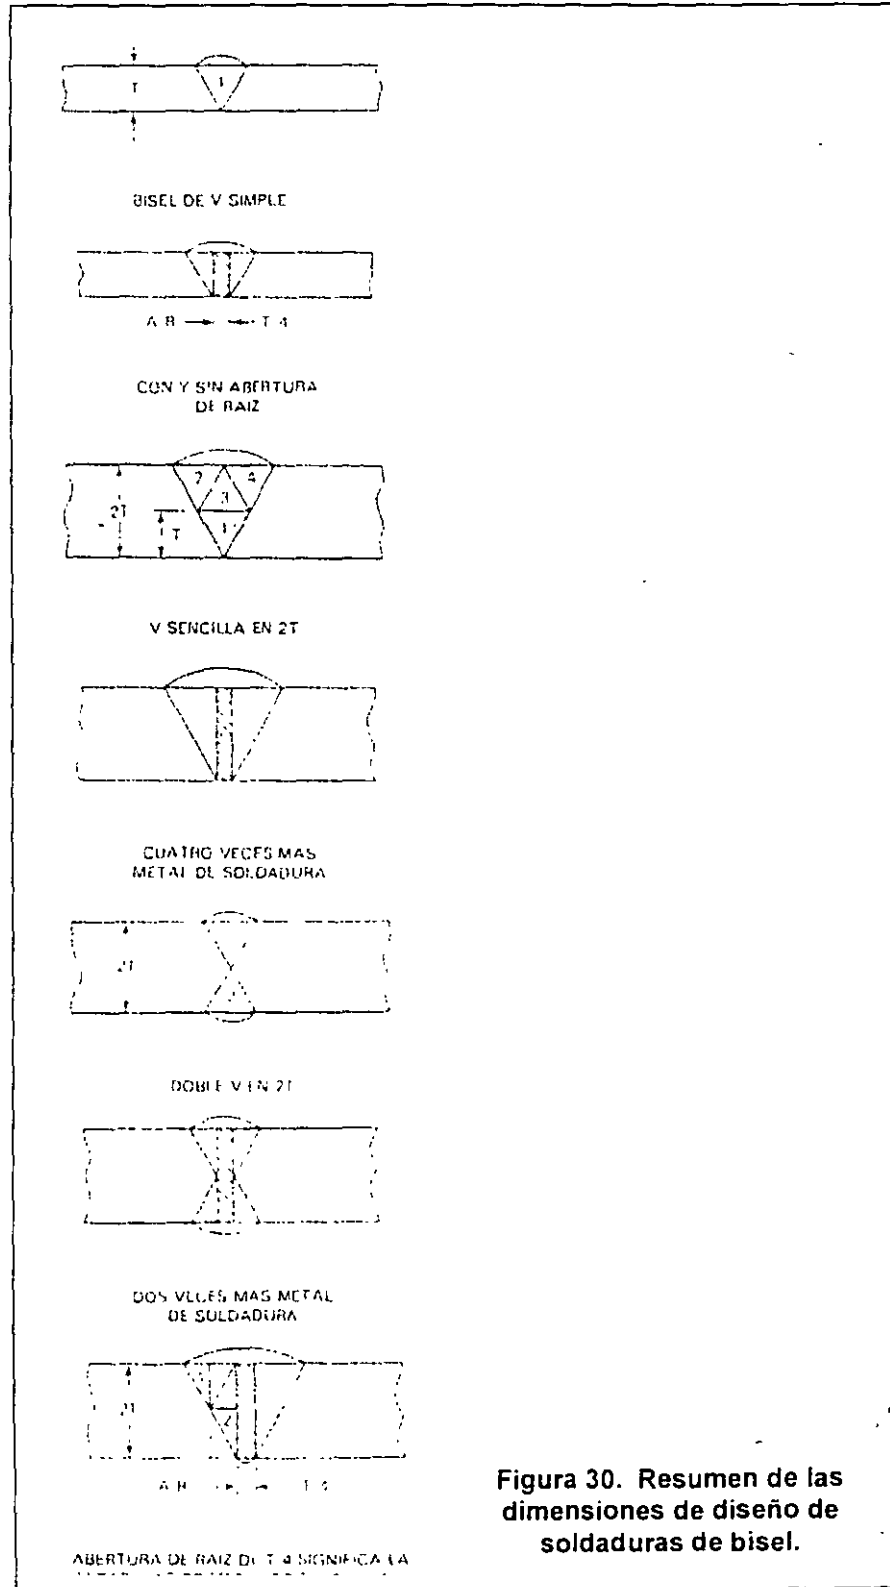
Resumen de las dimensiones de diseño de soldaduras de bisel.
